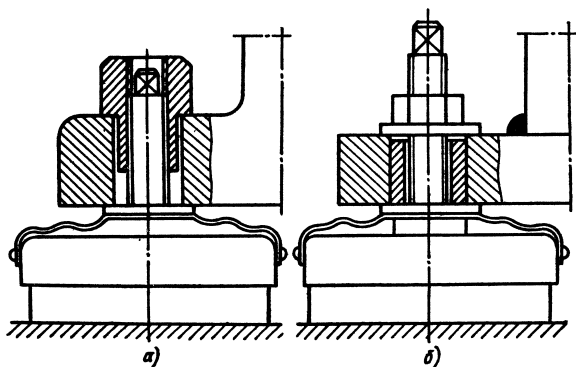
Установка оборудования на виброизолирующих опорах с креплением:
